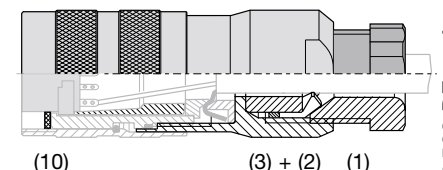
PG-Verschraubung montiert, Steckverbinder komplett
